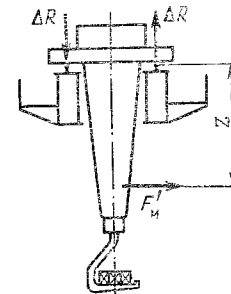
Схемы к расчету нагрузок на опоры тележки при жестком подвесе груза
